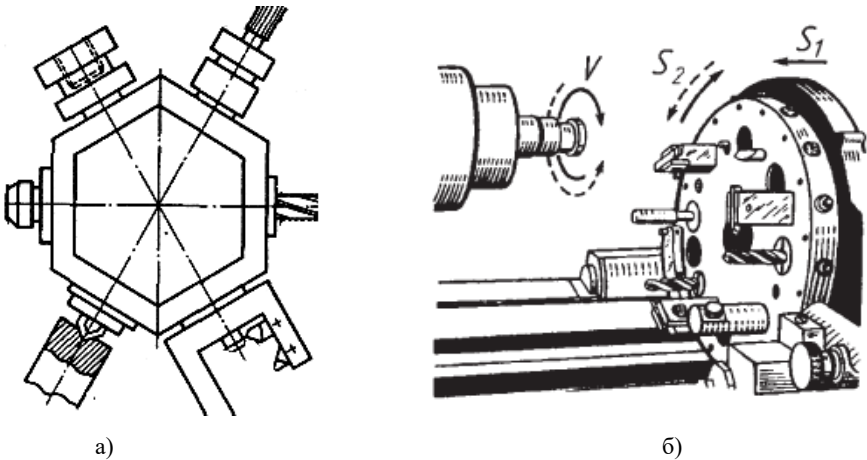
Револьверні головки токарно-револьверних верстатів
